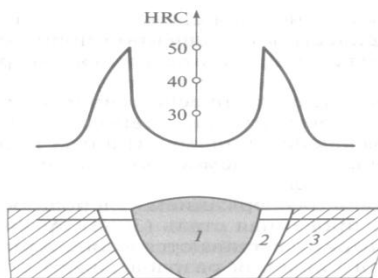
Распределение твердости после термической сварки стали 40ХФА: 1 - сварной шов; 2 - зона термического влияния; 3 - основной материал свариваемых заготовок
